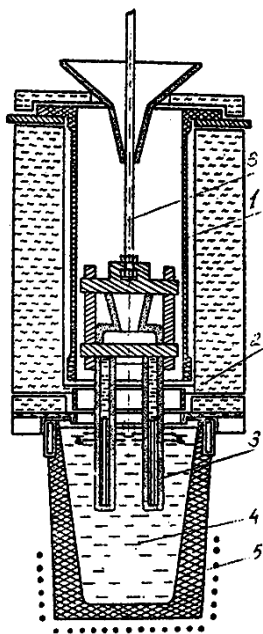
Схема установки УВНК: 1- вакуумная плавильная камера, 2 - жидкометаллический кристаллизатор, 3- печь подогрева форм, 4-каретки с подвесками форм, 5- привод вертикального перемещения форм, 6- плавильный индуктор для плавки мерной шихтовой заготовки.
